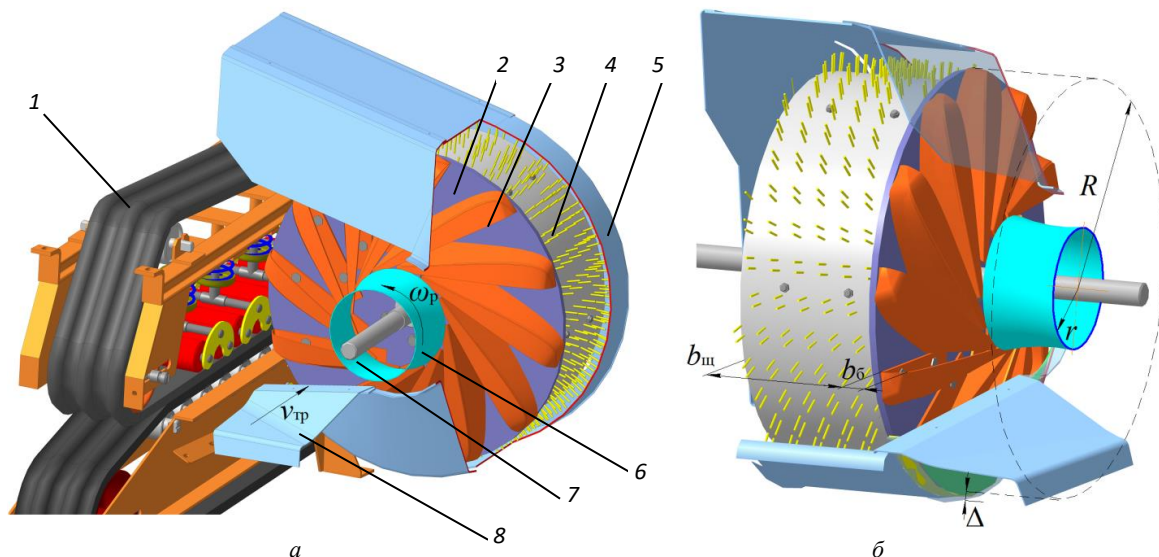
Конструкция роторного бильно-вычесывающего устройства: *a* – общий вид устройства; *б* – общий вид ротора; 1 – зажимной транспортер; 2 – ротор; 3 – бичи; 4 – вычесывающе-транспортирующая щетка; 5 – кожух; 6 – кольцо; 7 – вал ротора; 8 – стол
